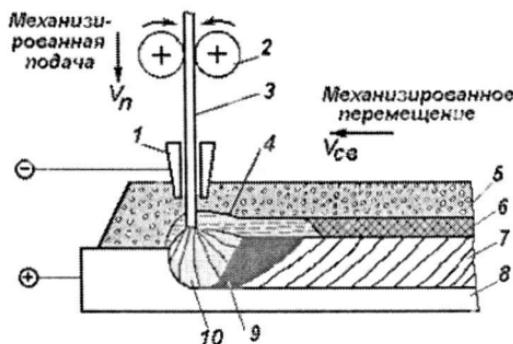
Схема процесса автоматической дуговой сварки под флюсом
